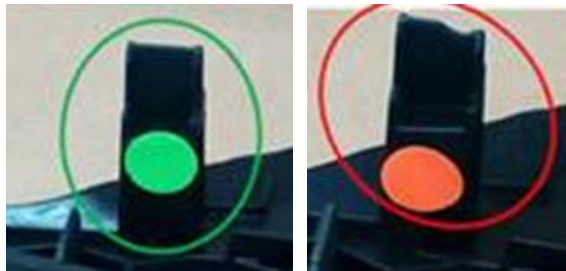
Pieza correcta (izquierda) y pieza con tiro corto (derecha)
